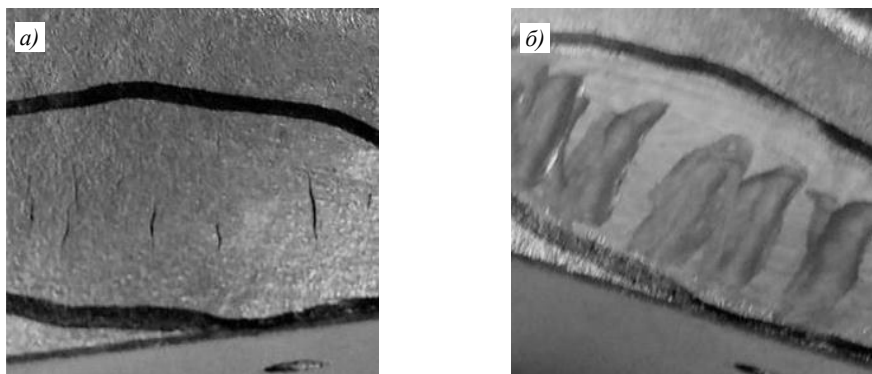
Внешний вид трещин (а) и мест их зачистки (б) на поверхности фрагментов сопловых лопаток из сплава марки ЖС6У
